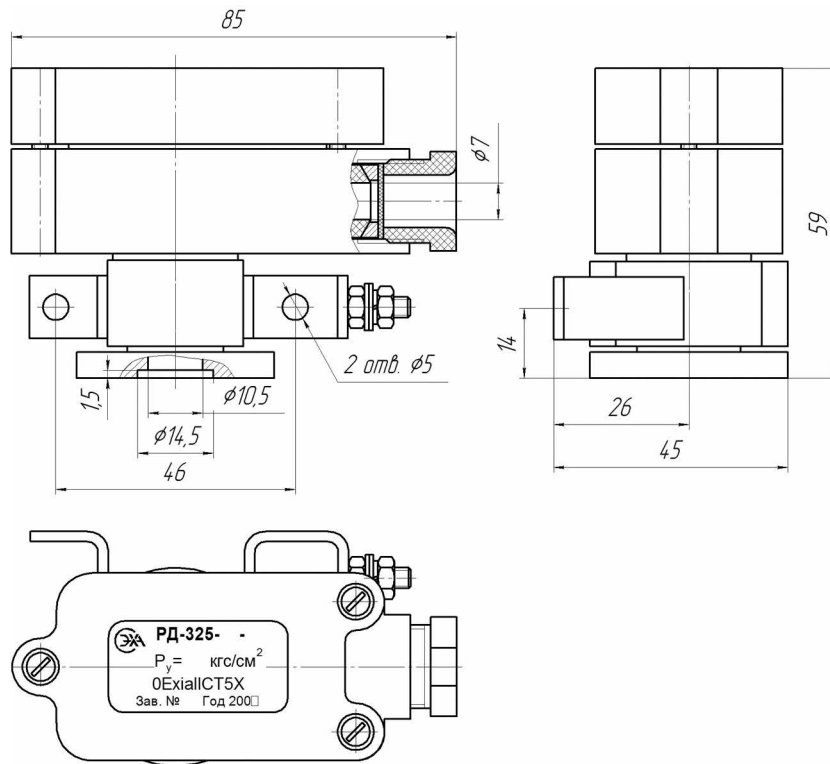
Габаритные и установочные размеры реле давления РД-325
